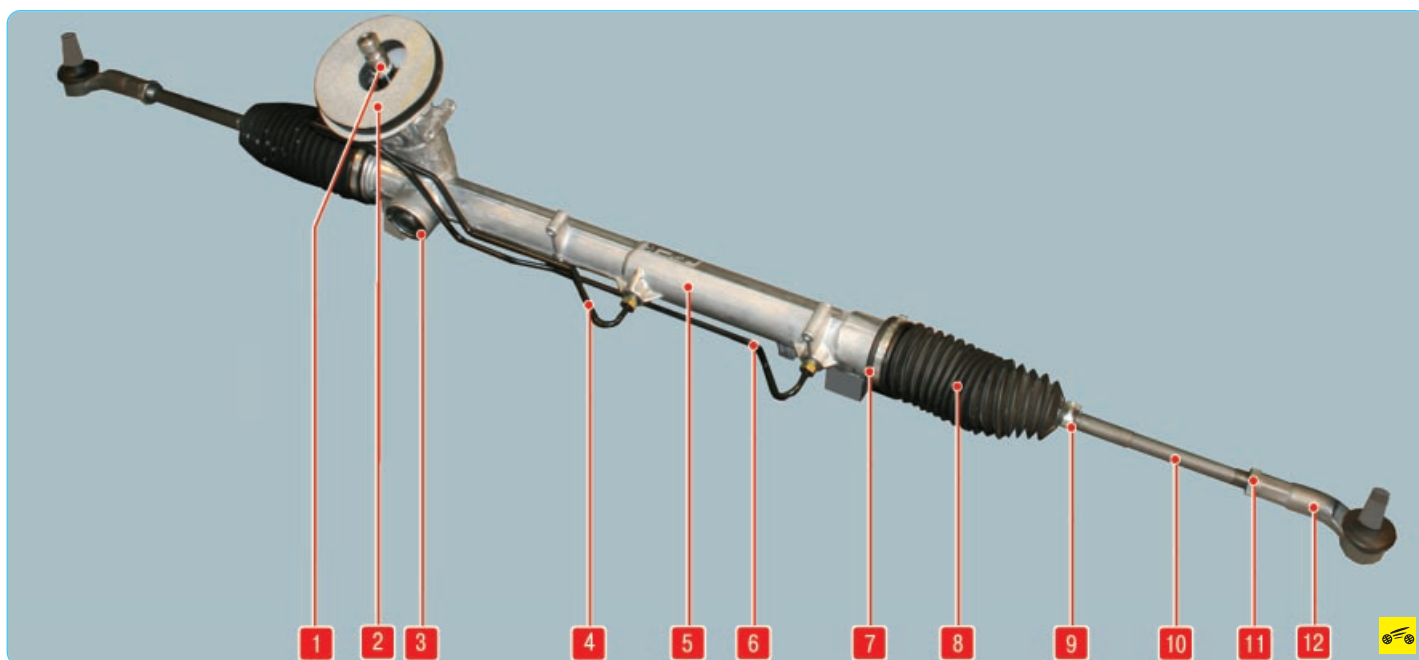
Рулевой механизм с гидроусилителем: 1 – вал рулевого управления; 2 – уплотнитель; 3 – регулировочная гайка; 4, 6 – трубопроводы; 5 – картер рулевого механизма; 7, 9 – хомуты чехла; 8 – защитный чехол; 10 – рулевая тяга; 11 – контргайка; 12 – наконечник рулевой тяги
